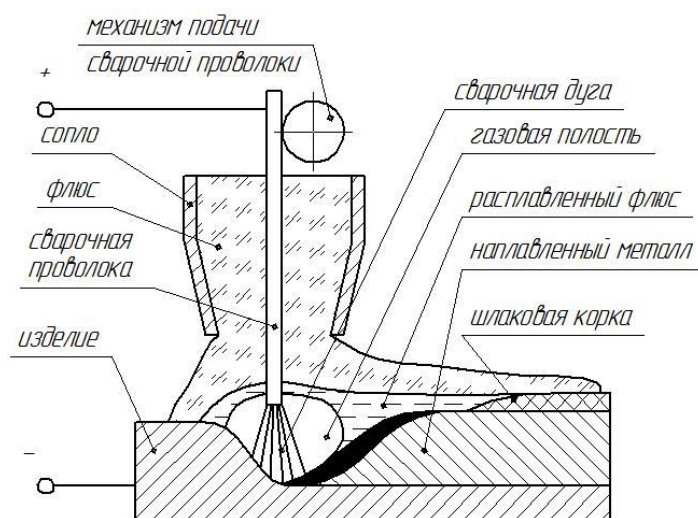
Схема осуществления автоматической сварки под флюсом
